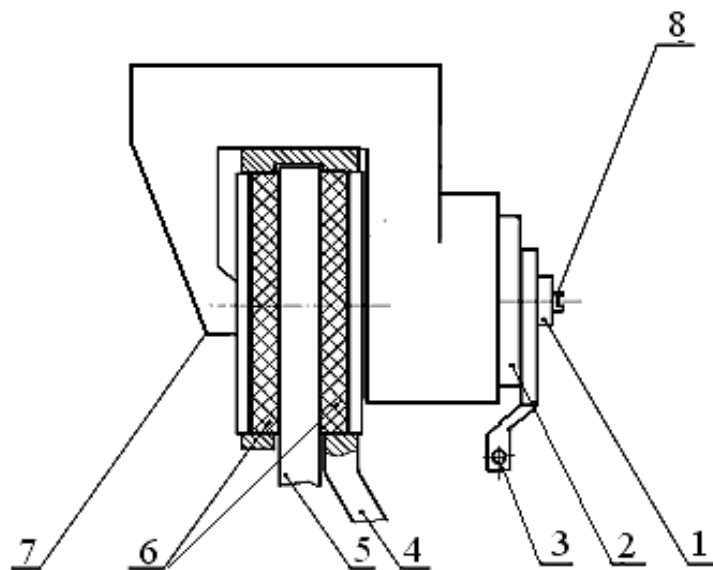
Дисковый тормоз с механическим приводом: 1 – гайка; 2 – механическое нажимное устройство; 3 – рычаг; 4 – корпус; 5 – диск; 6 – колодка; 7 – скоба; 8 – шпилька
